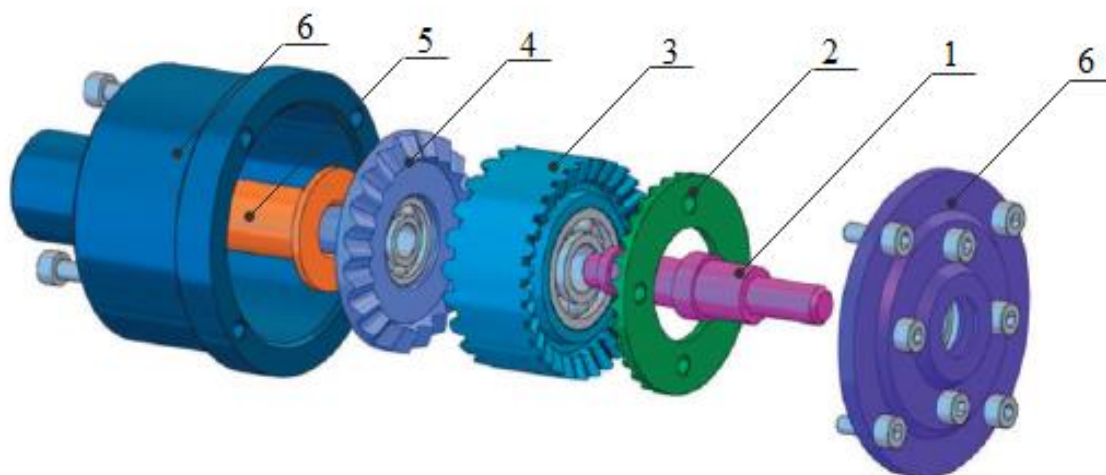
Виртуальная 3D-модель волнового торцевого кинематического редуктора: 1 – ведущий вал (генератор волн); 2 – неподвижное колесо; 3 – блок шестерен; 4 – подвижное колесо; 5 – ведомый вал; 6 – корпус редуктора
